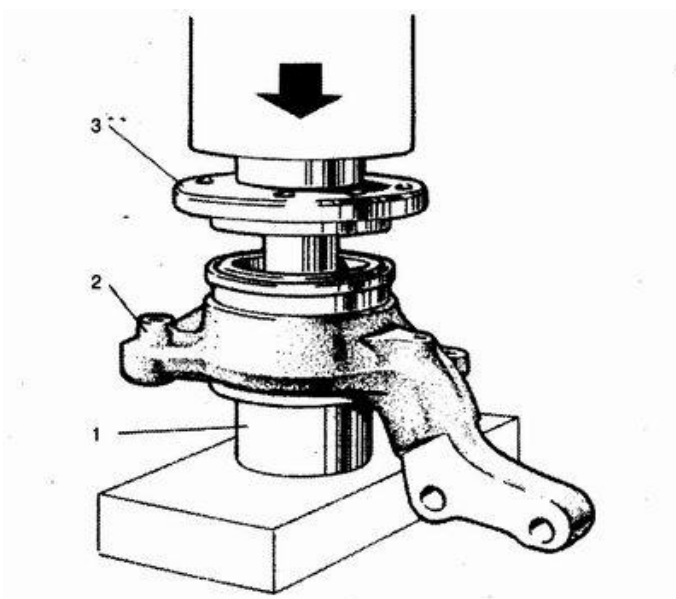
Порядок запрессовки ступицы колеса
